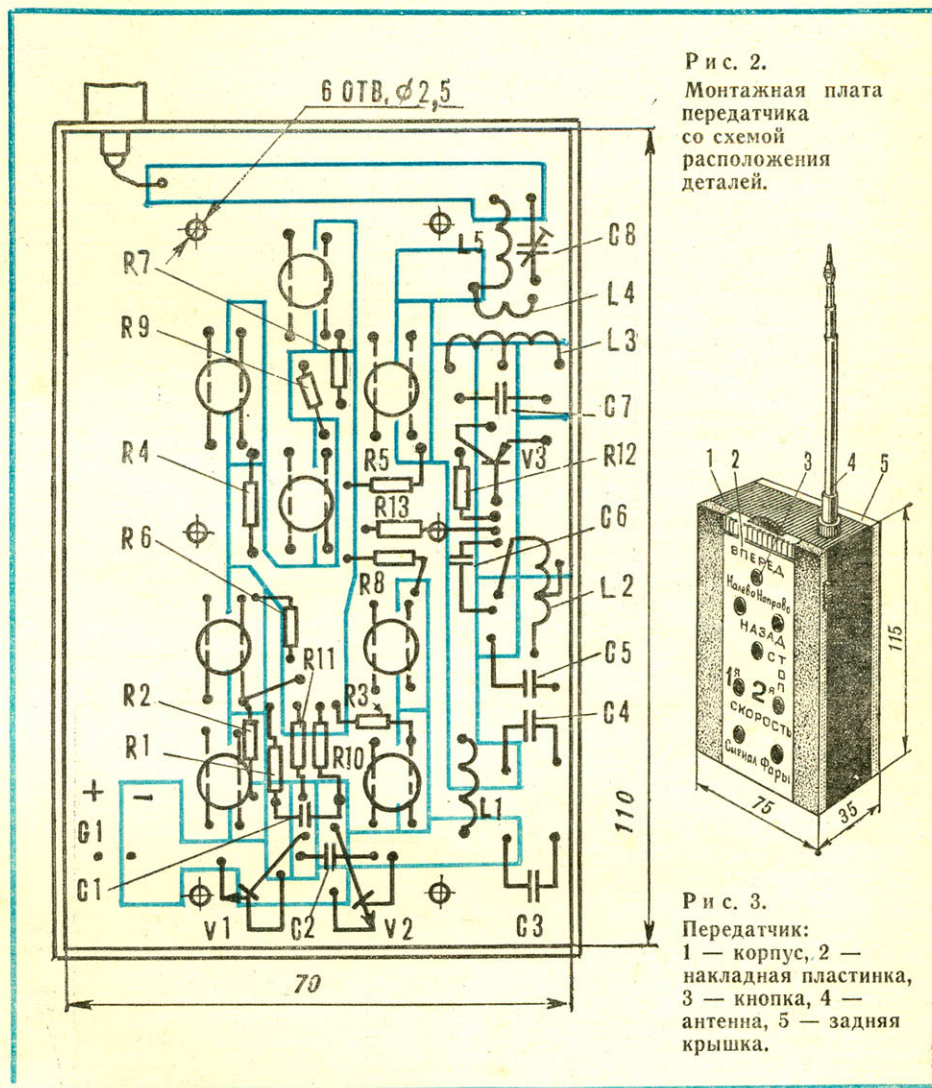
Монтажная плата передатчика со схемой расположения деталей.
